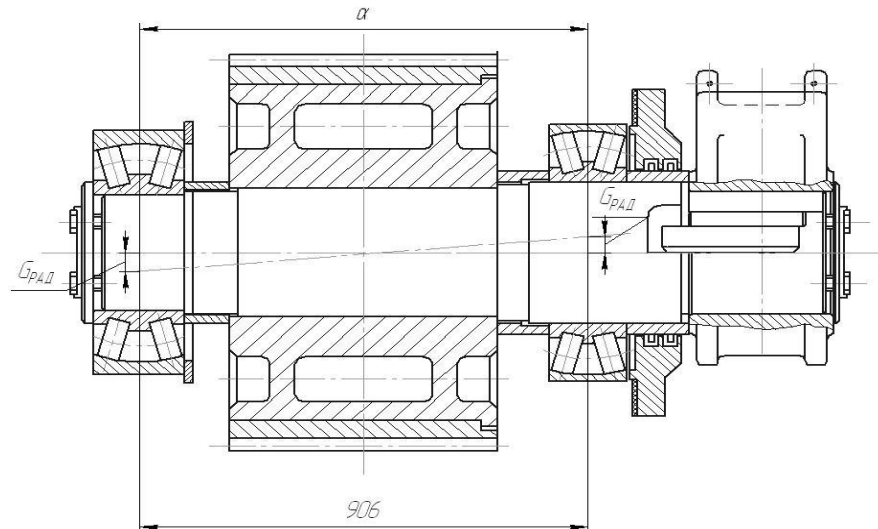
Схема вузла Ножевий вал нижній
